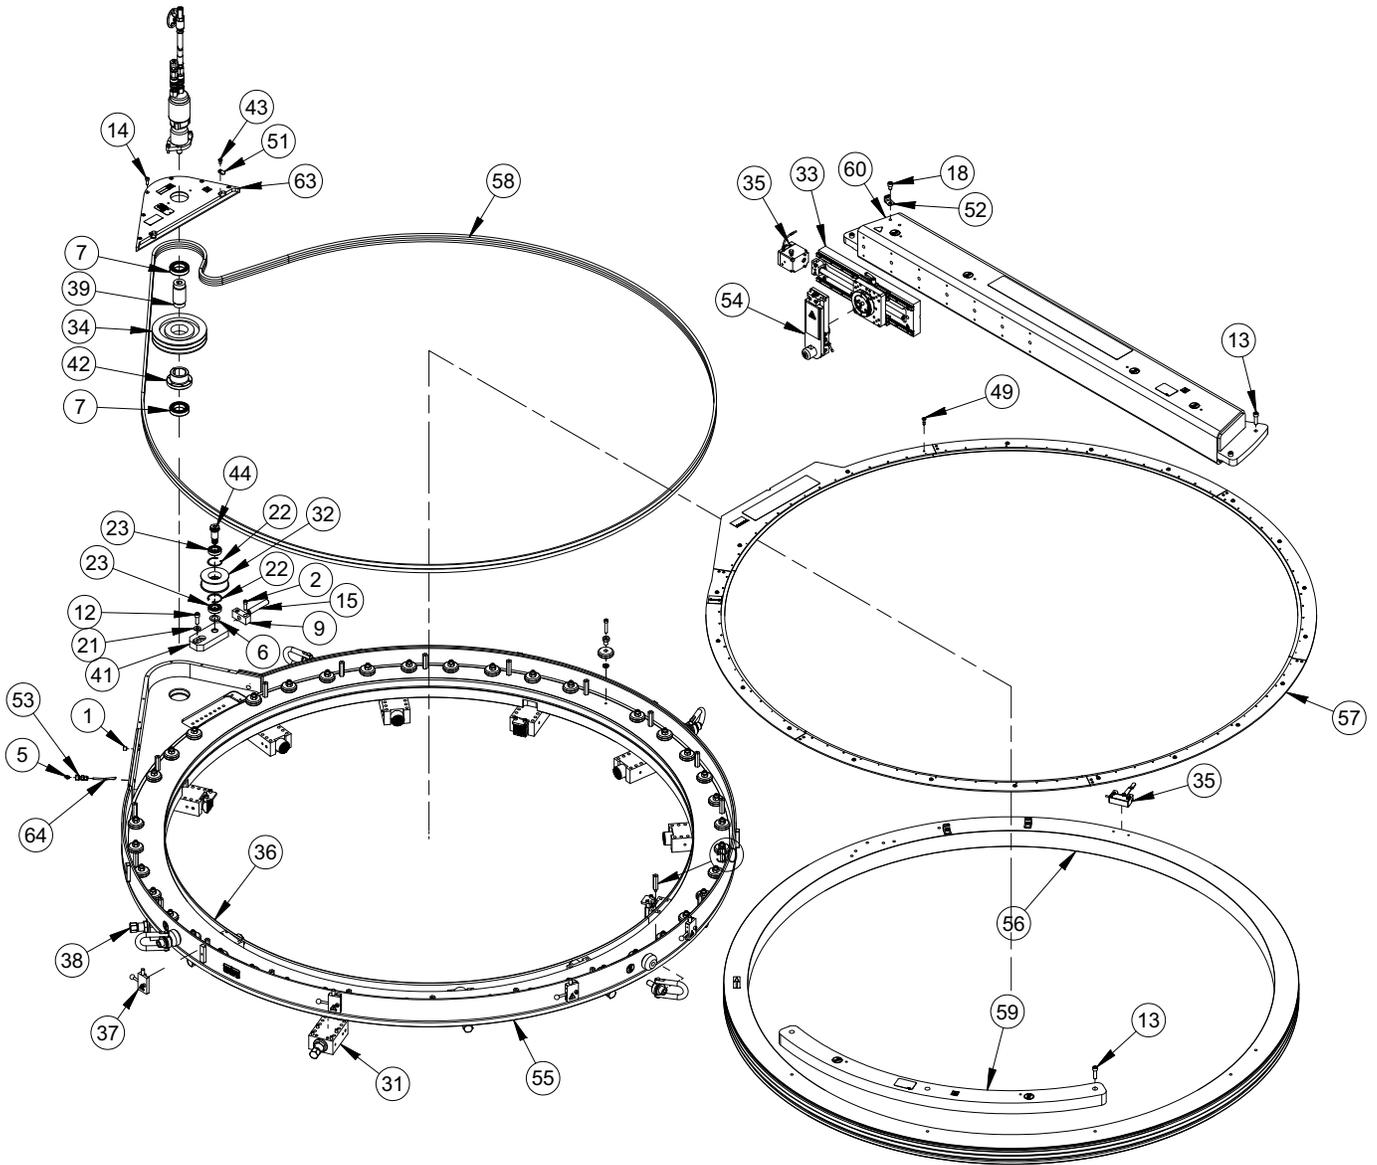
ODF80 SPEED FACER ENSEMBLE 1 (RÉF. 94770)
